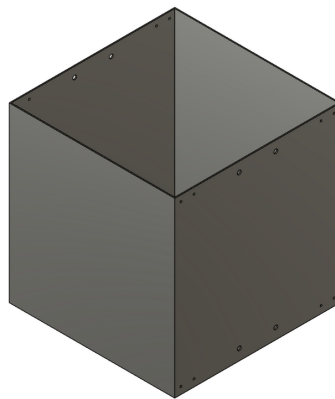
Vista isométrica da placa de ACM que será utilizada como parede após o desbaste e dobra.
